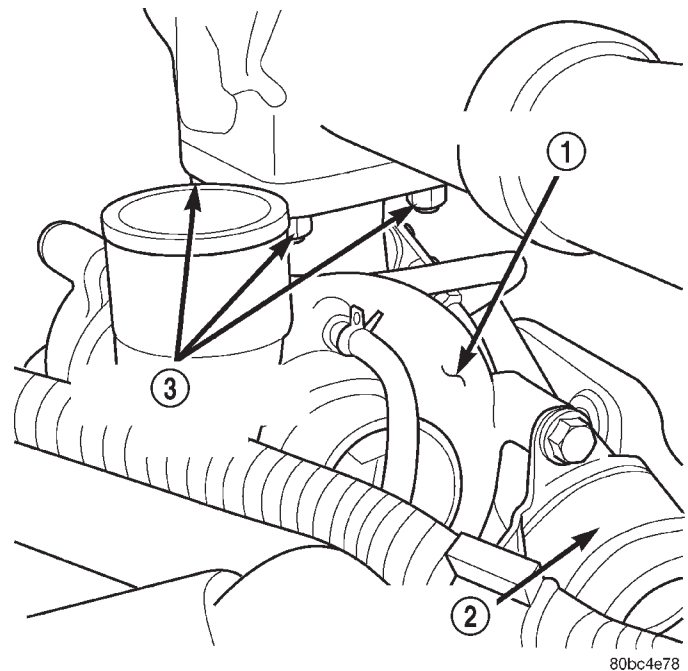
Befestigungsmutter auf Turbolader-Rückseite
